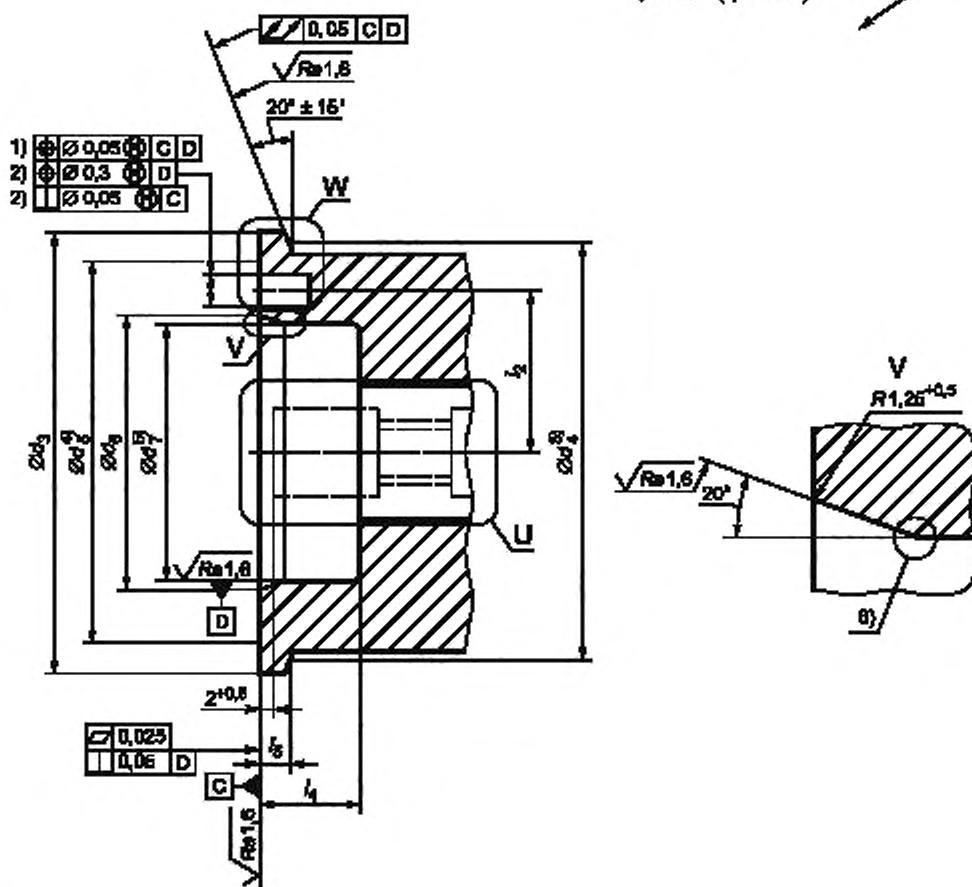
Конструкция и размеры фланцев приводов агрегатов и фланцев двигателя/редуктора (лист 1)
